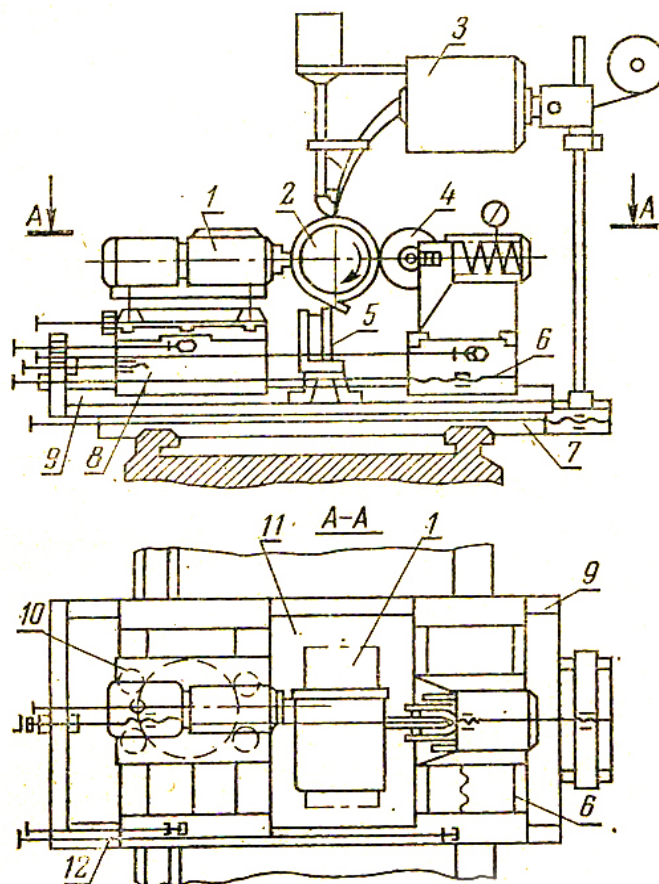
Схема установки для наплавки цилиндрических деталей под флюсом с одновременным фрезерованием и накаткой роликом: 1 — фрезарная головка; 2 — обрабатываемая деталь; 3 — наплавочная головка; 4 — накатной ролик; 5 — шлакоудаляющее устройство; 6 — суппорт накатной головки; 7 — карета токарного станка; 8 — суппорт фрезерной головки; 9 — поперечные направляющие; 10 — каретка с подъемными винтами; 11 — несущая плита; 12 — продольные направляющие.
